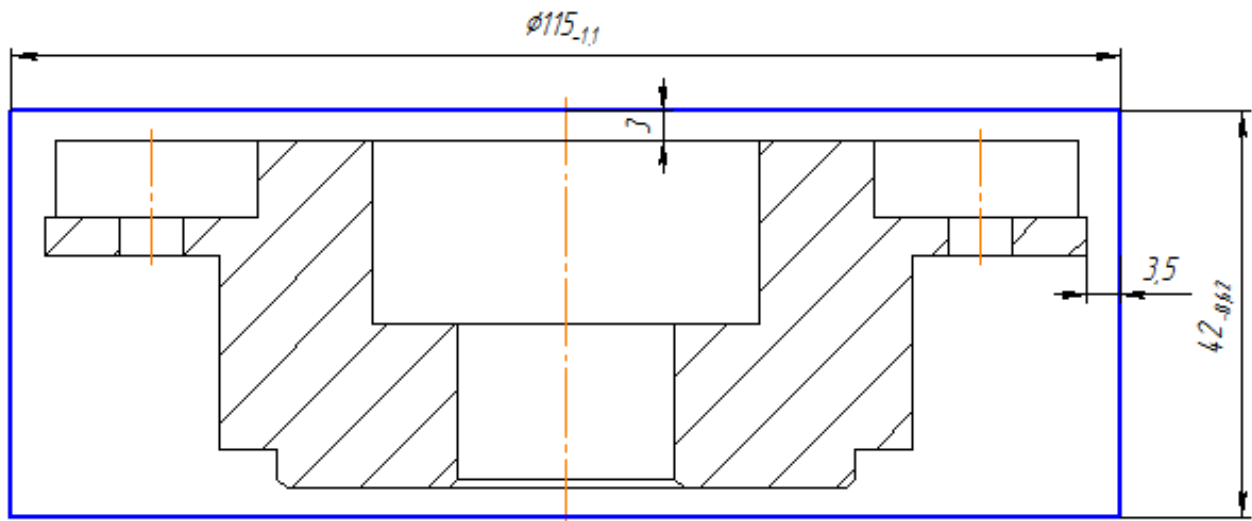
Ескіз заготовки з круглого прокату
